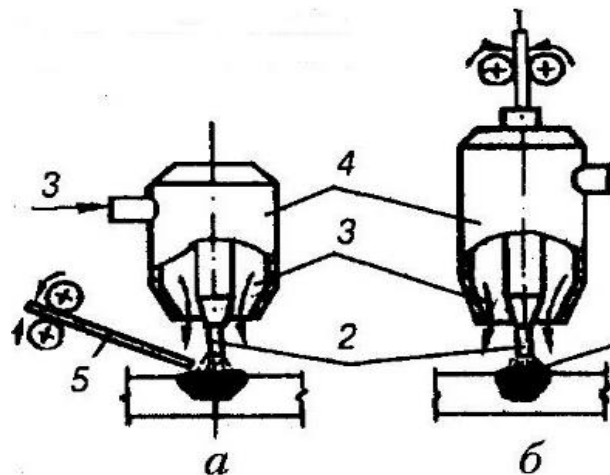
Схеми зварювання в середовищі захисних газів: а) плавким електродом; б) неплавким електродом; 1 – зварювальна дуга; 2 – електрод; 3 – захисний газ; 4 – газове сопло пальника; 5 – зварювальний дріт
